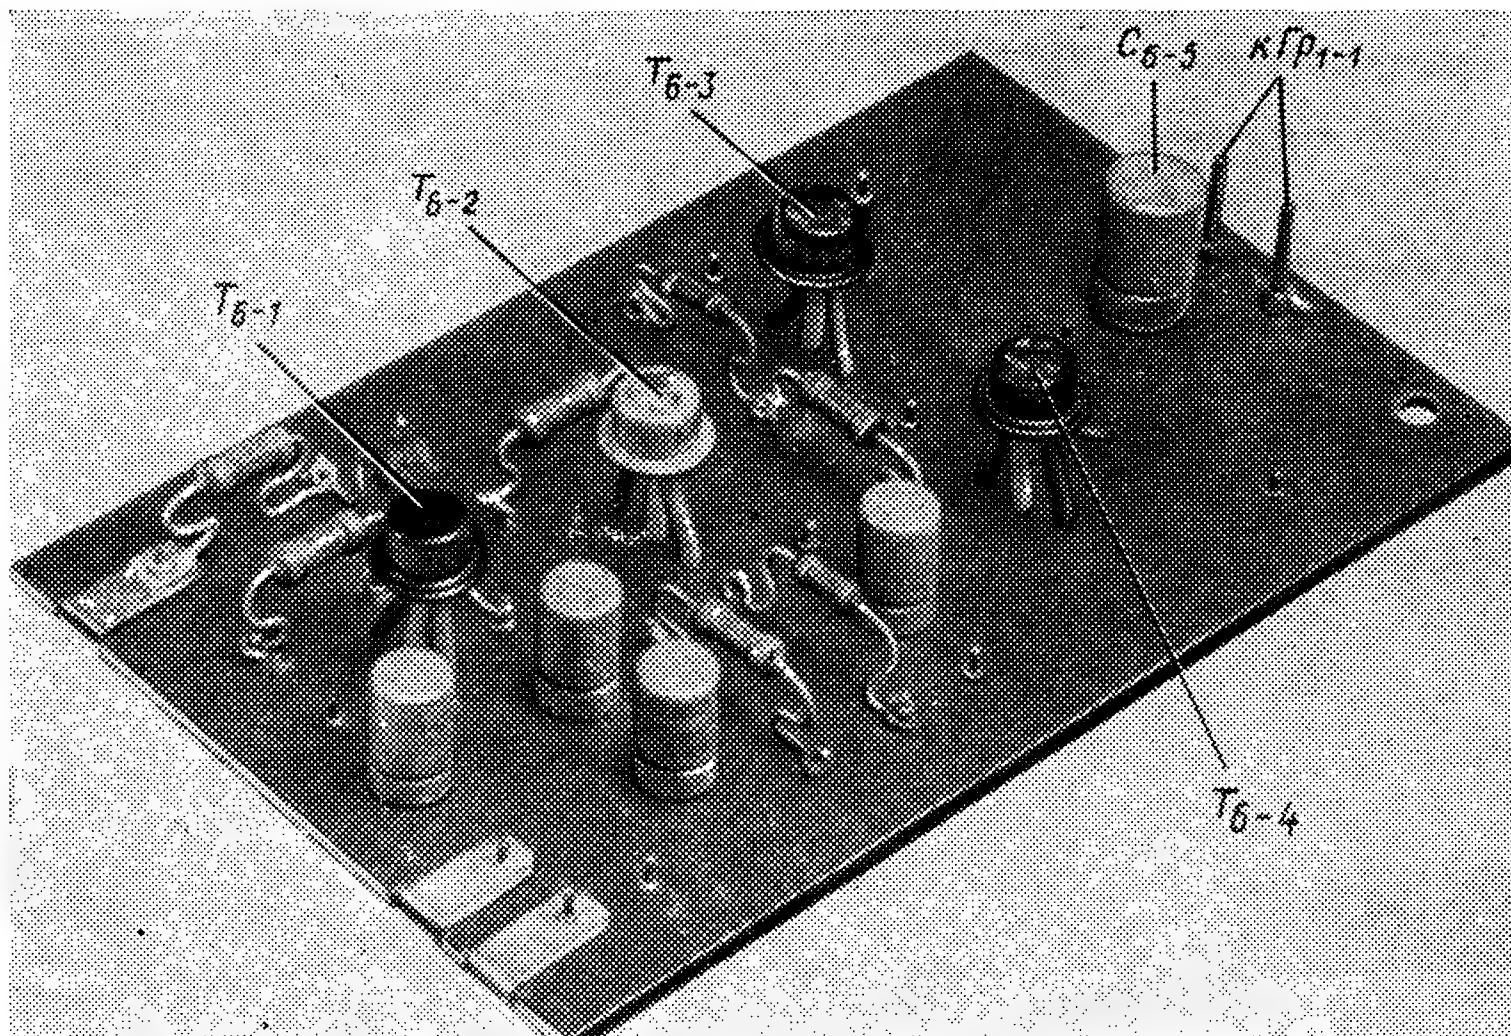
Внешний вид блока 6 и схема соединений его деталей на монтажной плате.
